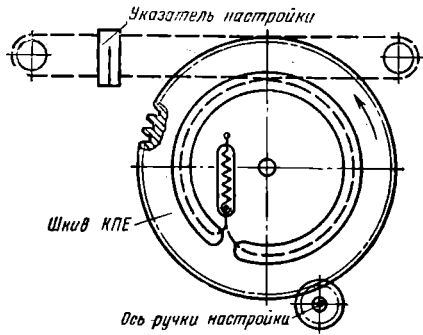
Кинематическая схема верньерного устройства радиоприемников «Сокол-404» и «Сокол-405»
